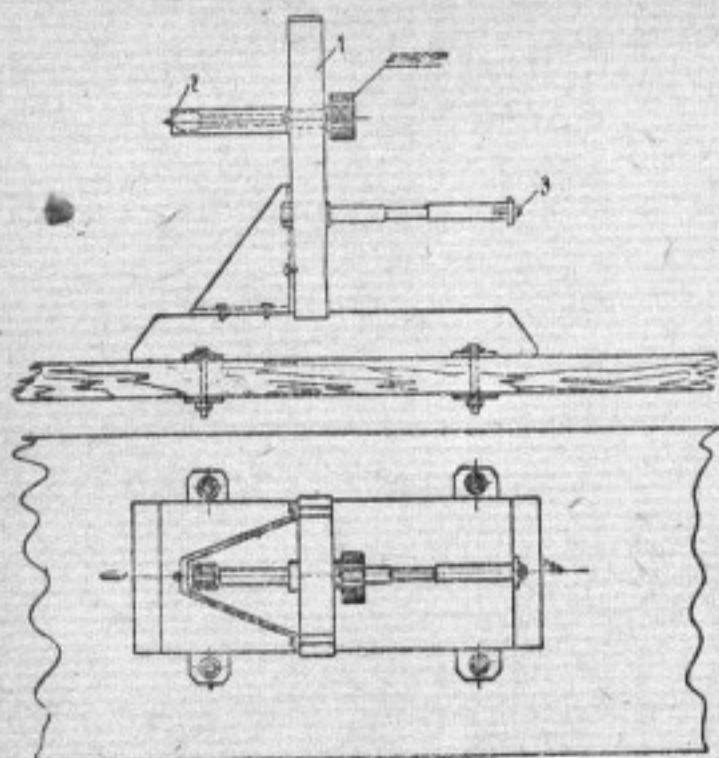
Приспособление для определения износа контршaftной шестерни коробки передач ГАЗ
